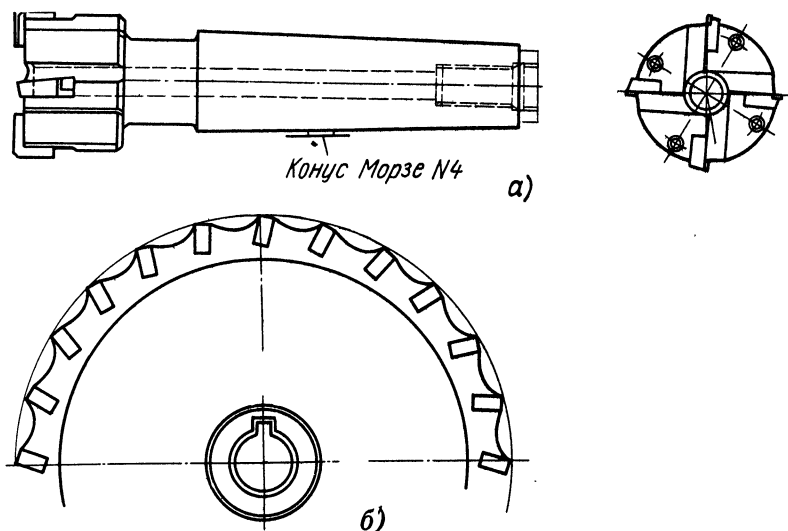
Фрезы конструкции И. Д. Леонова с пластинками твердого сплава:
